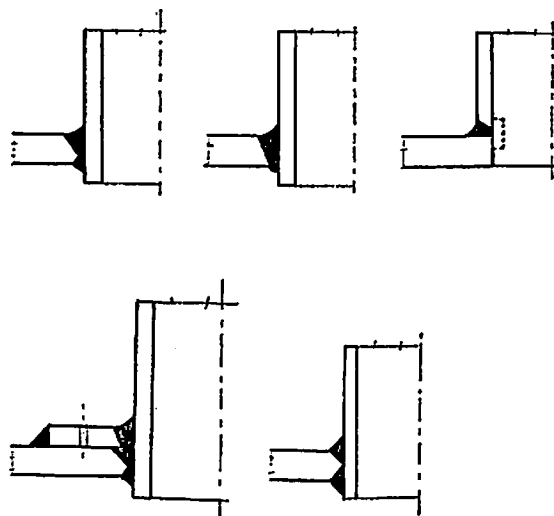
Welding details for Domes and Branches (文献-32)
